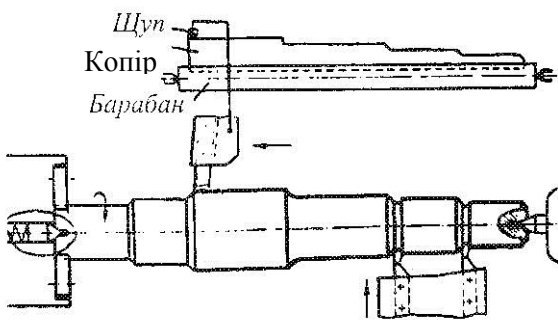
Схема обробки заготовки на токарному гідрокопіювальному напівавтоматі
